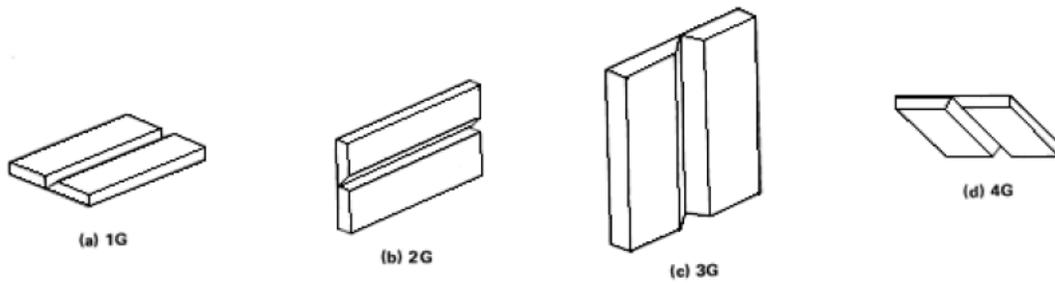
POSICIONES DEL ENSAYO PARA SOLDADURA EN RANURA.
